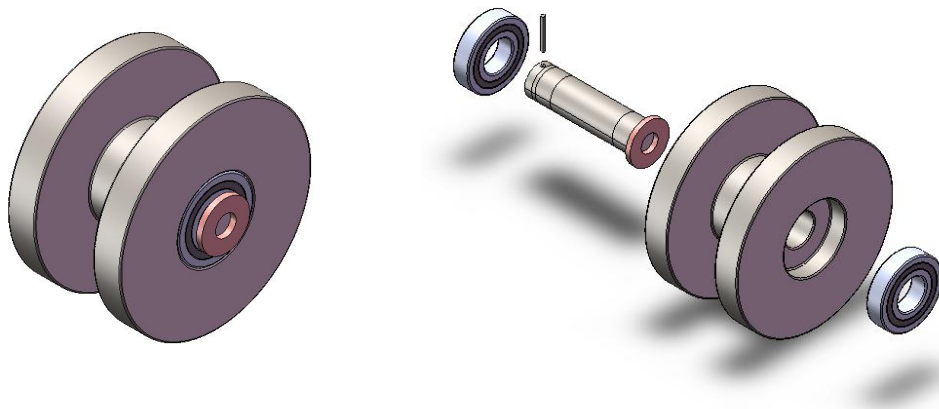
Despieza del conjunto masa, pasador y rodamiento.
